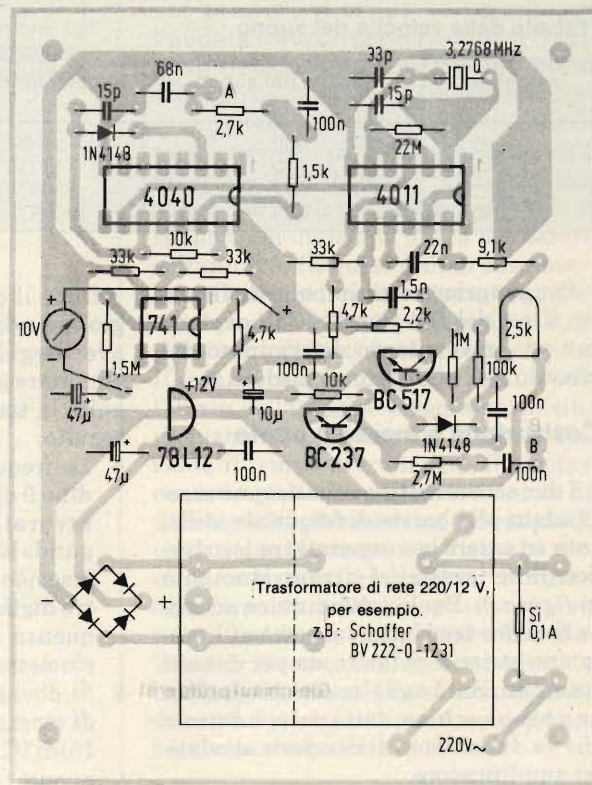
Disposizione dei componenti sul circuito stampato.
